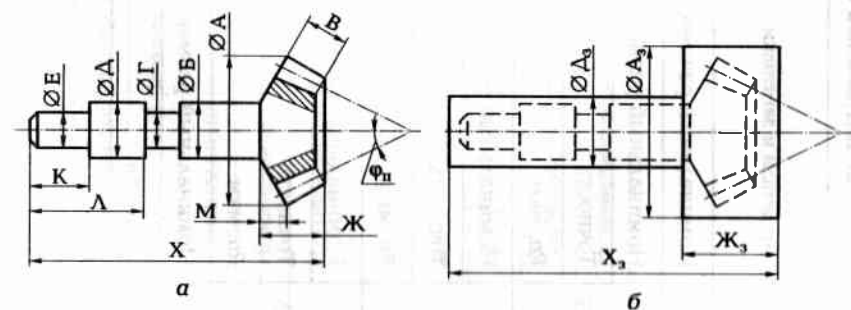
Эскиз обрабатываемого прямозубого конического зубчатого колеса типа «вал»:
